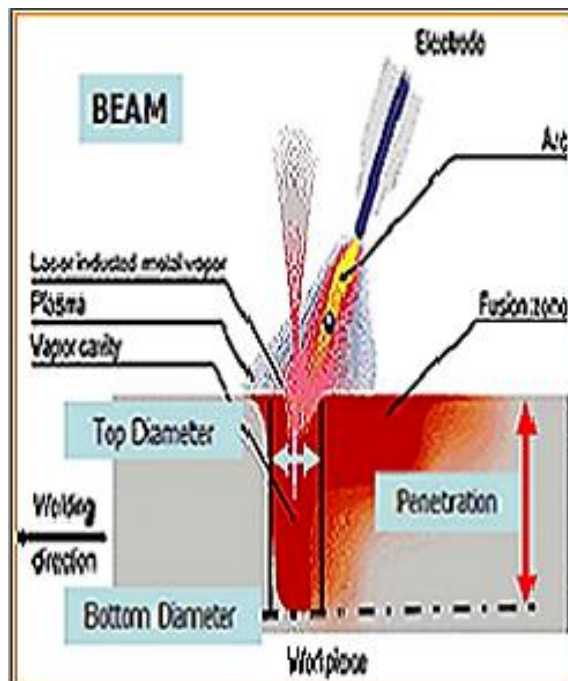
Propriedades físicas de um cordão de soldadura laser.
